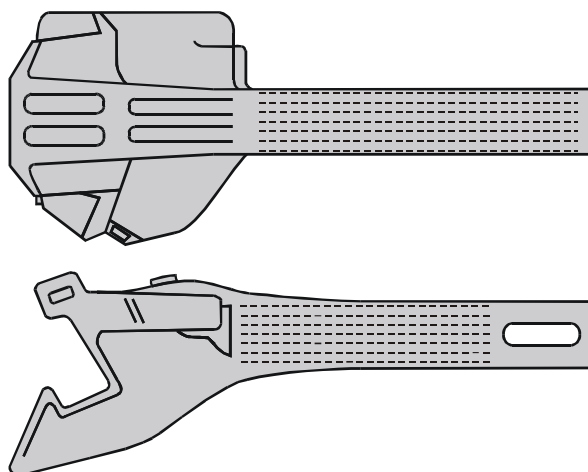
Схема сканирования хвостовика корпуса автосцепки
